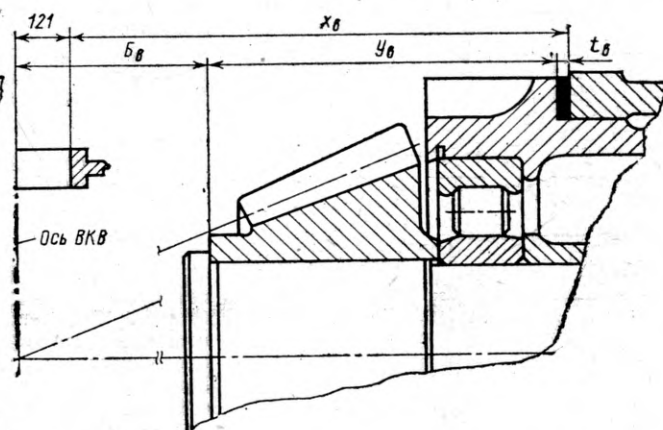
Измерение размеров для верхнего коленчатого вала: $Б_v$ — размер от торца шестерни до вершины конуса зубьев; $У_v$ — расстояние от торца шестерни до привалочной плоскости корпуса вертикальной передачи (замеряется на собранной передаче до постановки в блок); $Х_v$ — расстояние от посадочной плоскости в блоке дизеля для верхней передачи до постели коренных подшипников ВКВ; 121 — радиус постели для коренных подшипников ВКВ (в мм); t_v — толщина регулировочных прокладок
